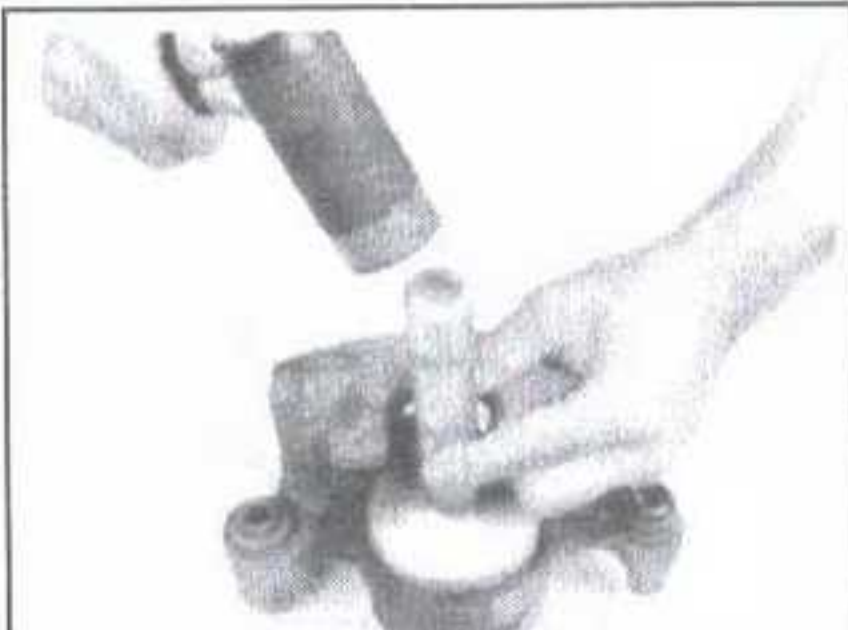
Запрессуйте пыльники в корпус суппорта при помощи выколотки и деревянного молотка
